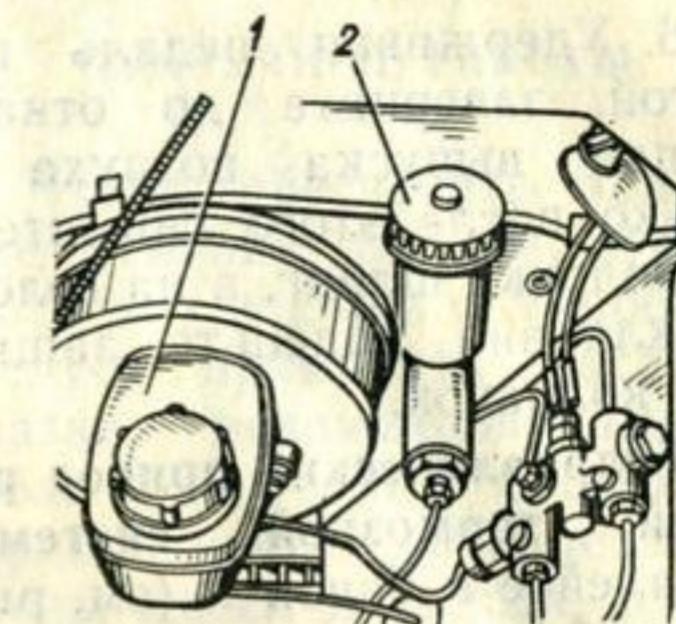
Бачки главных цилиндров гидроприводов выключения сцепления и рабочей тормозной системы:
